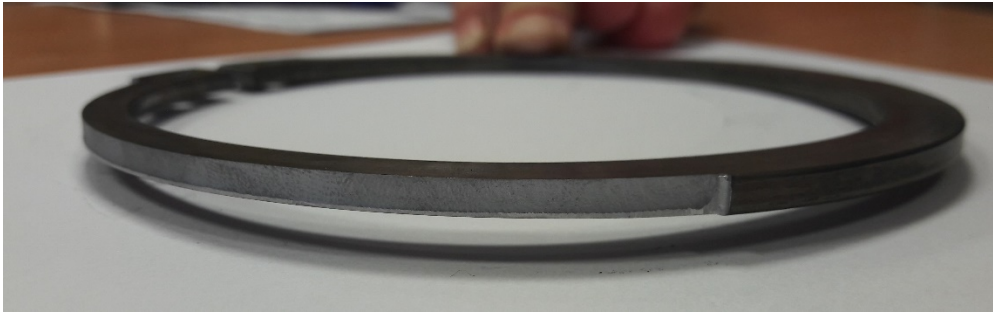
,23,24] Otlaky způsobené nečistotou v nástroji
